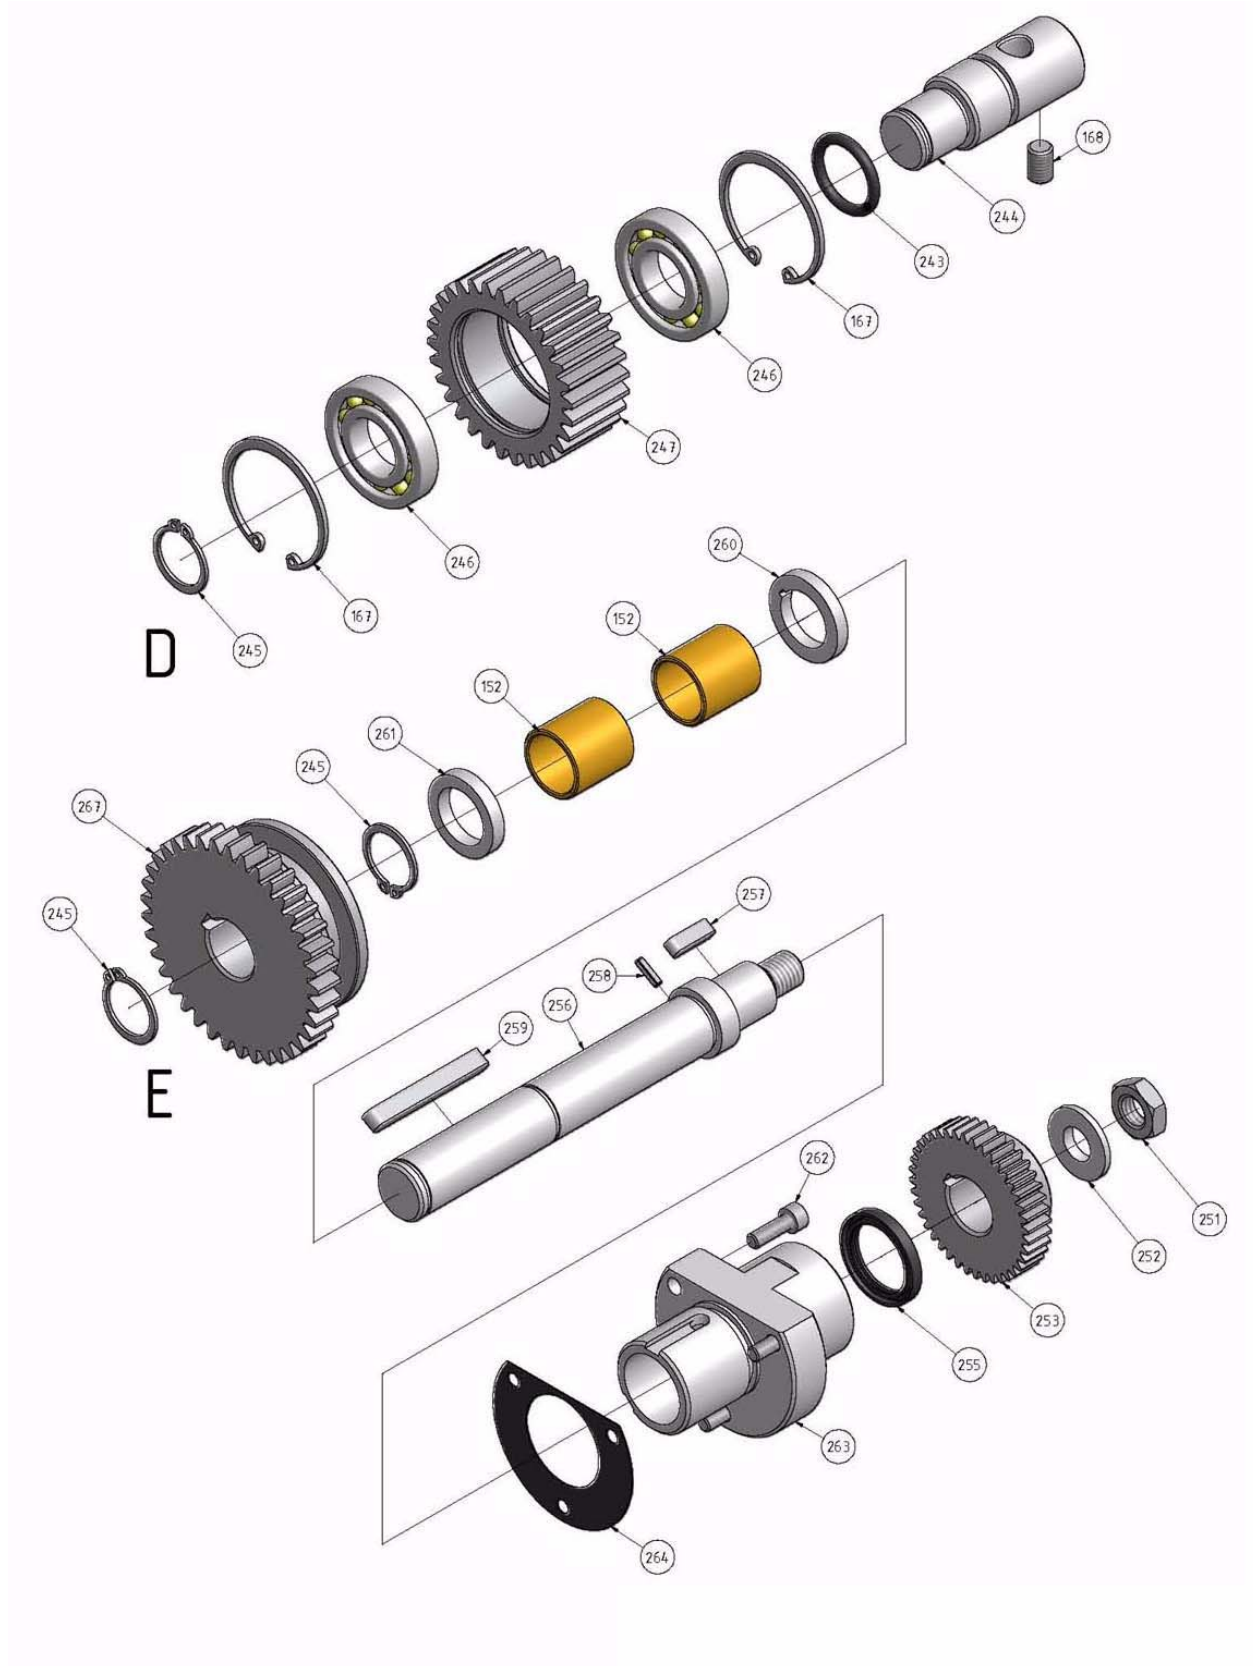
Getriebe Spindelstock 5-6 - Headstock gear 5-6
